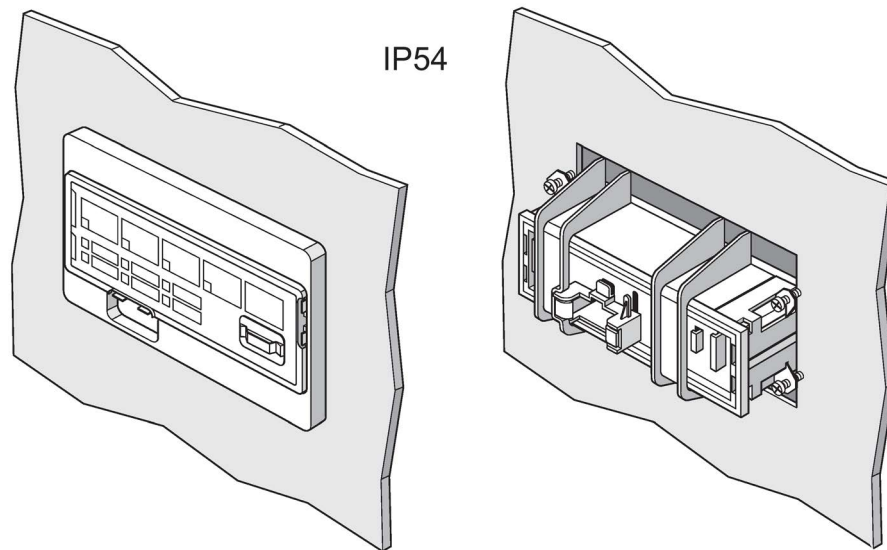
Montaje del adaptador para el módulo de mando (2)
